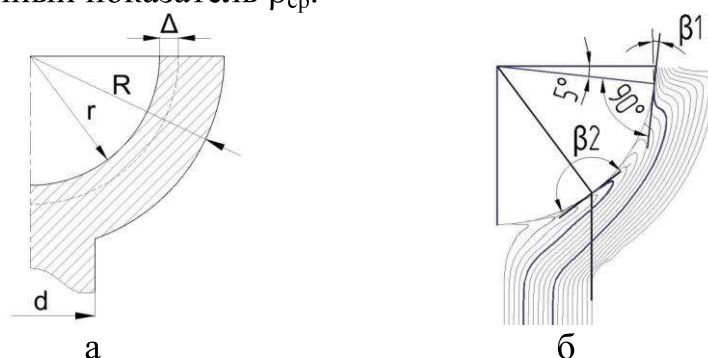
Поковка типа стержня с полусферическим фланцем а – принятые обозначения размеров б - схема измерения углов ориентации волокон β_1 и β_2
